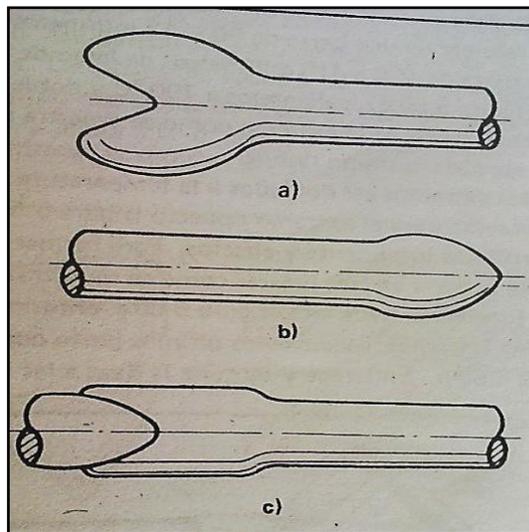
Horquilla y cuña o soldadura boca de caballo
